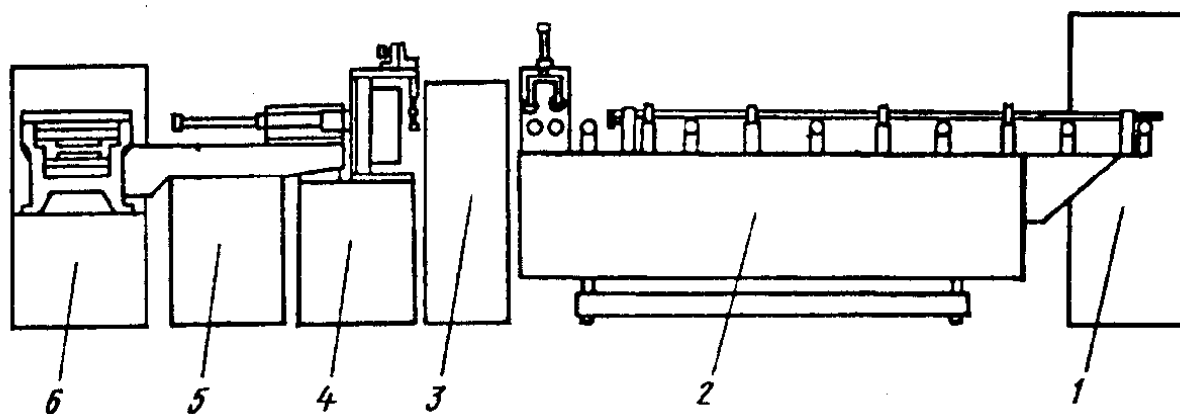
Схема комплекса горячей поперечно-клиновой прокатки
